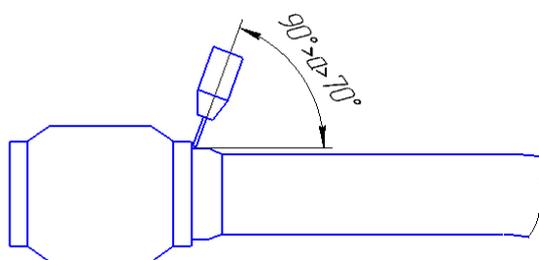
Сварка трубы передней и компенсатора
